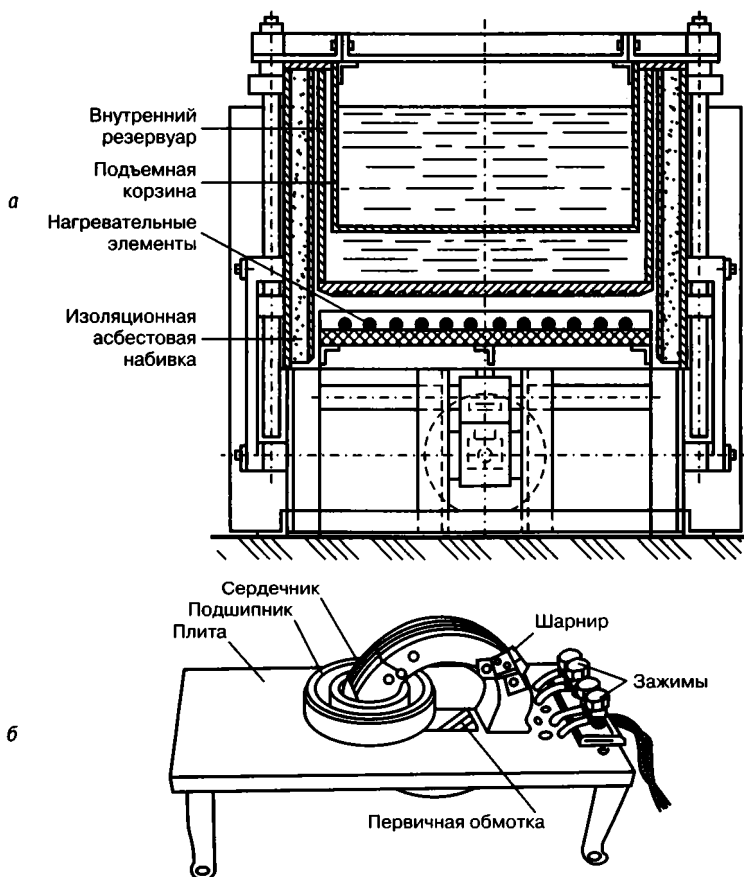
Приспособления для нагрева подшипников качения при посадке на вал электрической машины:
